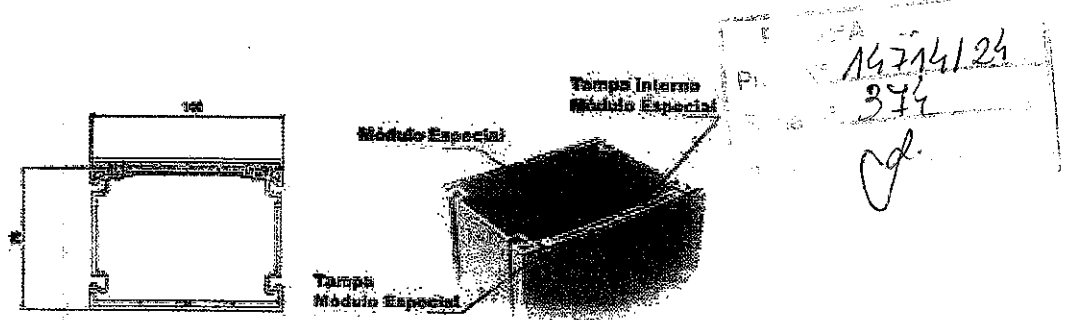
Esquema em planta do perfil canaleta dentro do módulo básico
